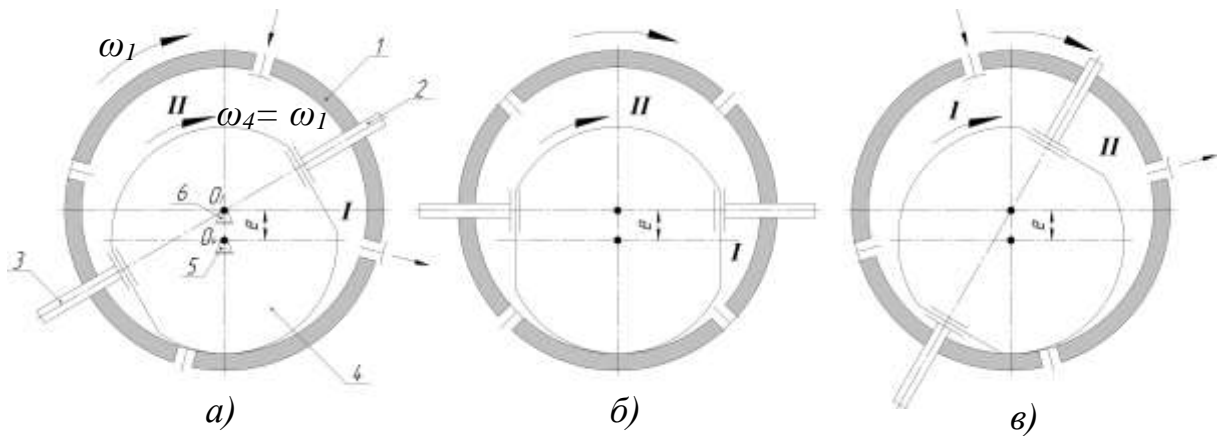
До розгляду особливостей конструкції і принципу дії компресора нового типу: 1 – зовнішній корпус з впускними і нагнітальними саморегульованими клапанами (обертається навколо осі O_1 з кутовою швидкістю ω_1); 2, 3 – шибери; 4 – внутрішній ротор (обертається навколо осі O_4 з кутовою швидкістю $\omega_4 = \omega_1$); 5, 6 – осі обертання O_1 і O_4 ; e – ексцентриситет
